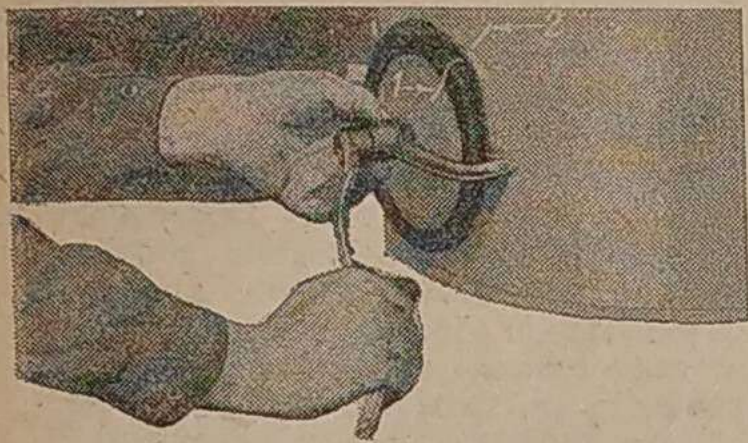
Метки для точной установки на место крышки люка газогенератора: 1 — метка на крышке, 2 — метка на корпусе.
